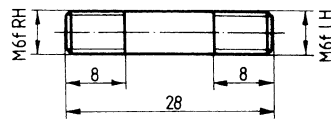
Links- und Rechtsgewinde an einem Teil (RH = right hand = rechts; LH = left hand = links).
